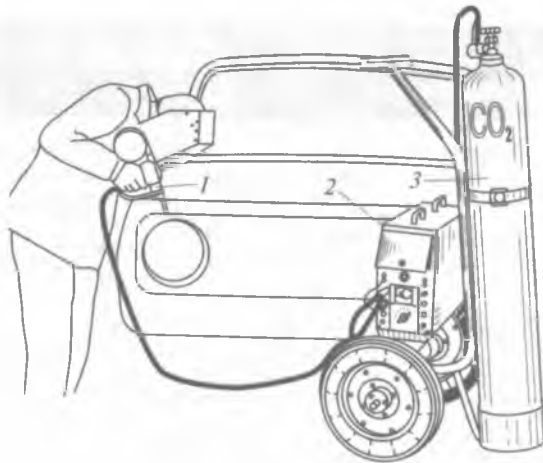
Общий вид передвижной полуавтоматической установки И-103 «Луч» для сварки в среде защитного (углекислого) газа:
